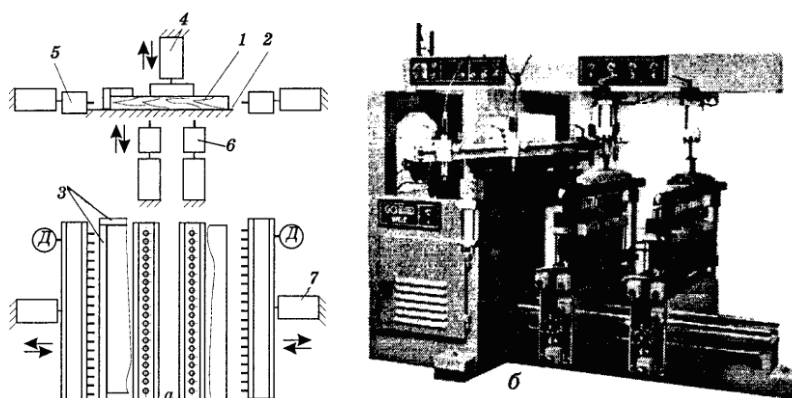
Позиційний багатошпиндельний вертикально-горизонтально свердлильний присадний верстат з набором горизонтальних і вертикальних головок: а – принципова схема; б – загальний вигляд; 1 – щит; 2 – стіл; 3 – напрямні; 4 – притискачі; 5 – горизонтальні багатошпиндельні головки; 6 – вертикальні багатошпиндельні головки; 7 – приводи переміщення
